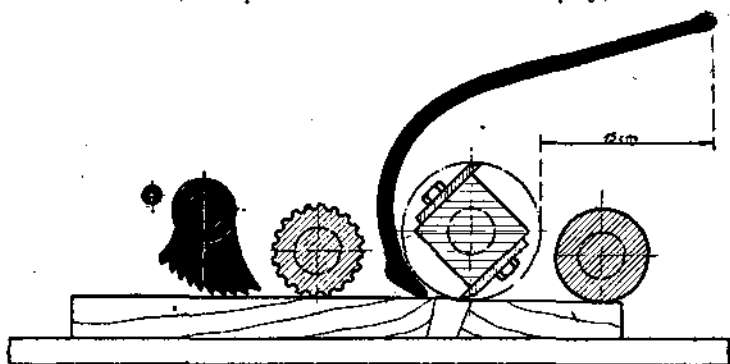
Внешний вид пропускного строгательного станка с предохранительными приспособлениями.
